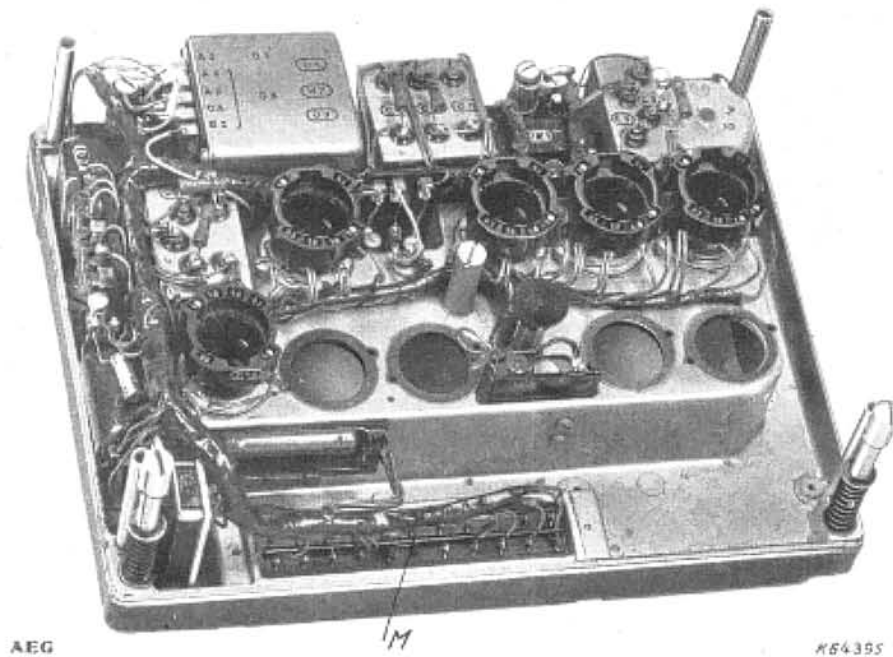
Geschweißtes Nachrichtengerät mit 74 Schweißstellen.
